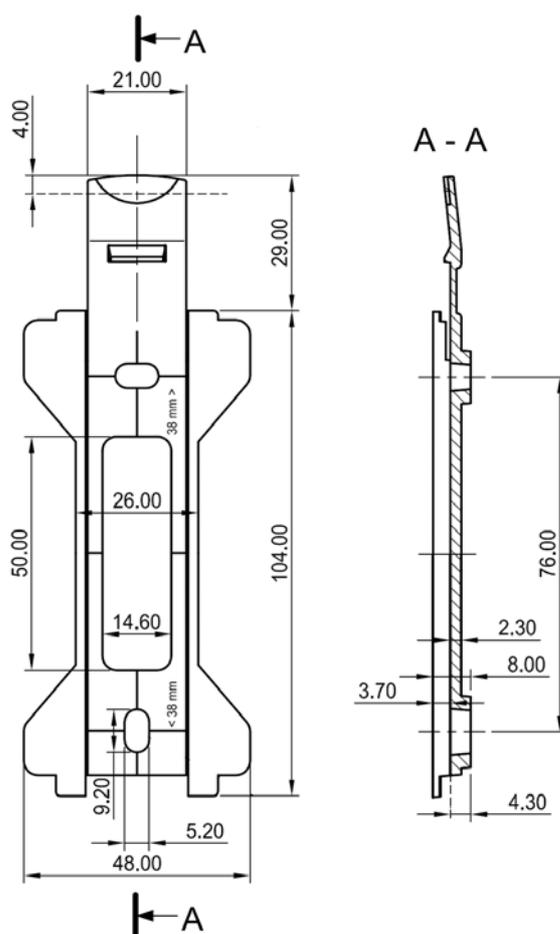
Приспособление для крепления ИТУС-ПСД-1 на стену
